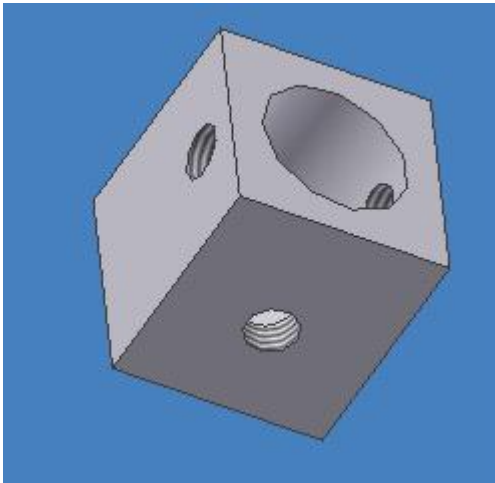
Pieza A1 . Se observa el mecanizado aplicado a 24 piezas según el plano AND00 - 0101
